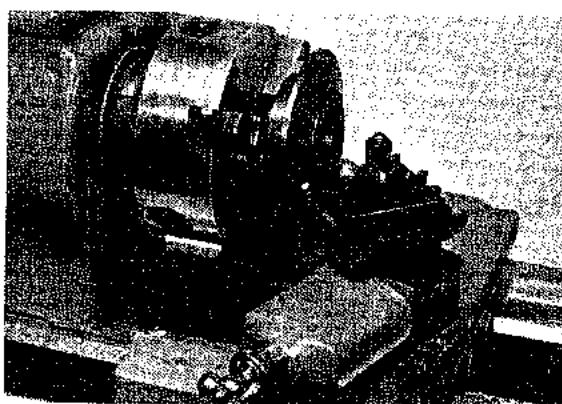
Torre de torno para cuatro herramientas (R. K. LeBlond Machine Tool Co.)
